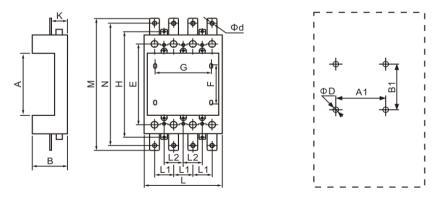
Габаритные и установочные размеры корзины втычного фронтального подключения КА-330E
